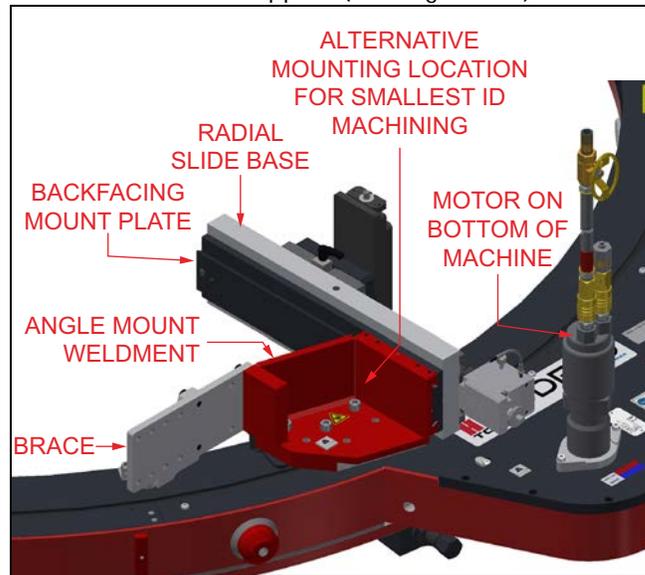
NOUVEL EMPLACEMENT DU MOTEUR ET EMPLACEMENT DU SUPPORT (ILLUSTRATION AVEC LA ODF80)
